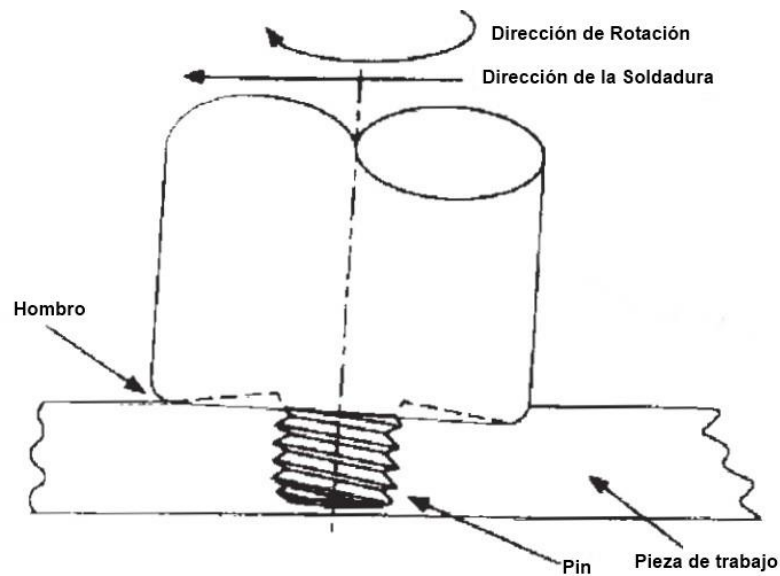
Diagrama de la herramienta de soldadura (34)
